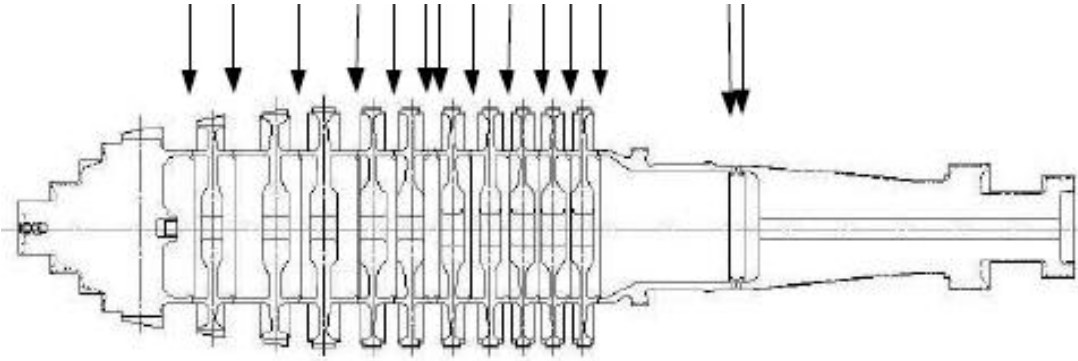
Arrangement général pour le rotor de compresseur complètement soudé de la puissance GT10B d'ALSTOM. Une série de soudures d'EB, comme indiquée par des flèches est employée pour construire le rotor. Les quatre disques à haute pression au côté droit sont faits de pièces forgées UDIMET-500 et sont EB soudé aux rotors austénitiques d'acier inoxydable.
